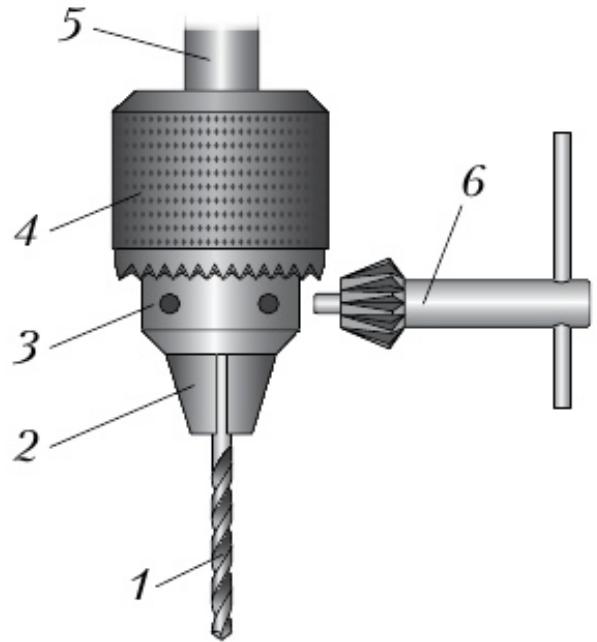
Трёхкулачковый патрон сверлильного станка: 1 – сверло; 2 – кулачки; 3 – втулка; 4 – кольцо с насечкой; 5 – шпиндель; 6 – ключ
